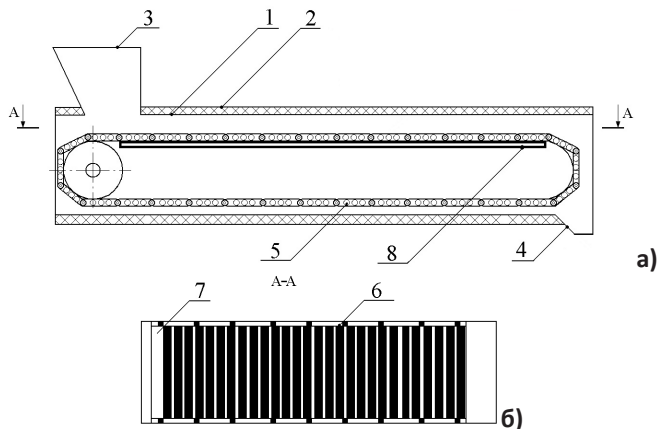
Конструкция предложенной жомосушилки непрерывного типа
